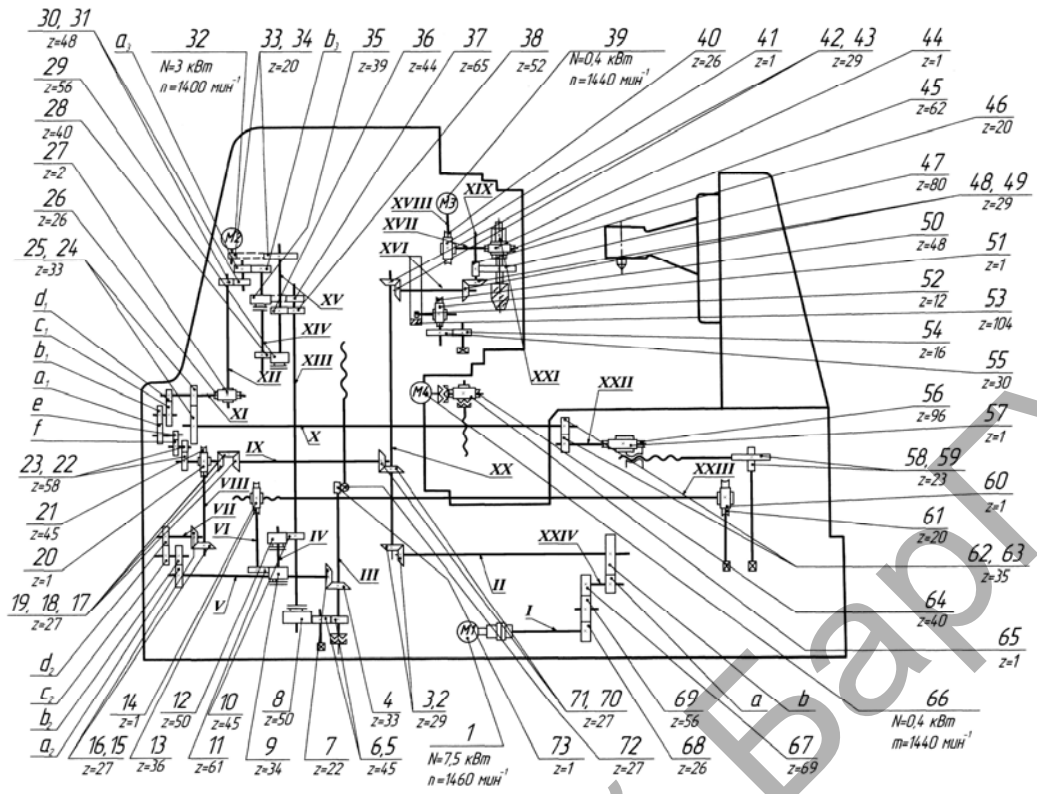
Кинематическая схема станка модели 5M324A
